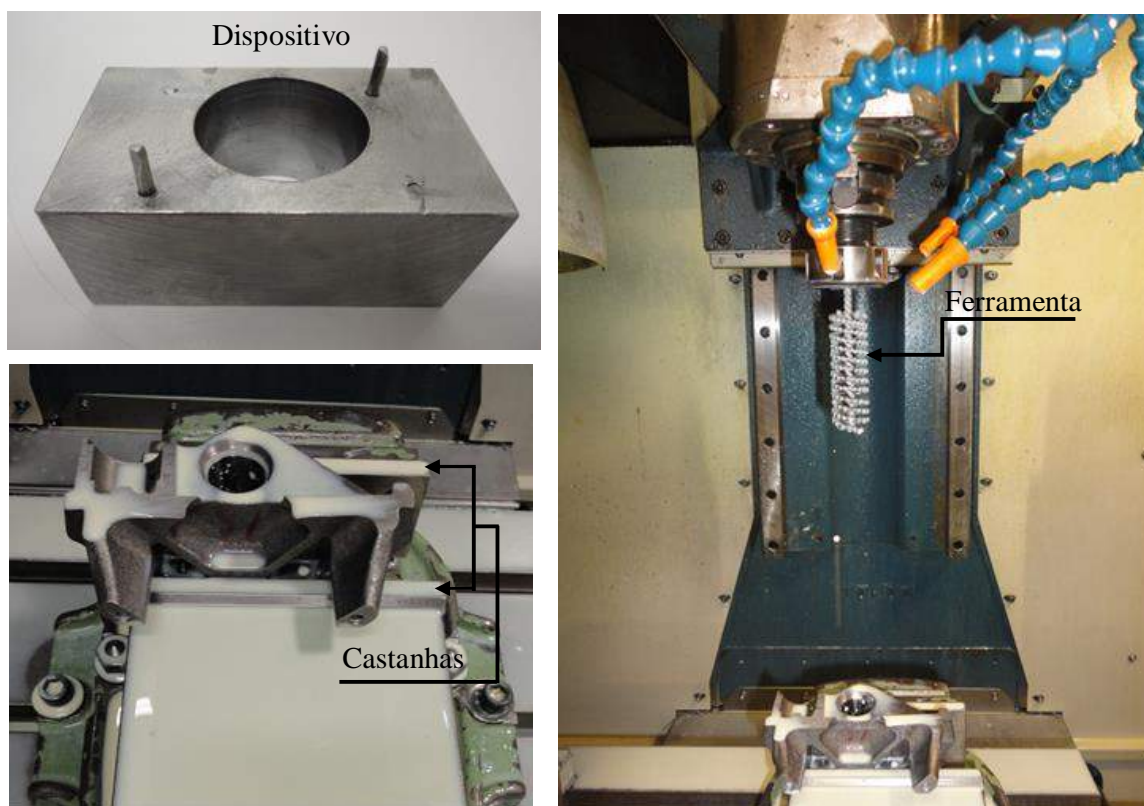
Dispositivo fabricado para fixação do bloco de um compressor hermético em uma fresadora CNC.
